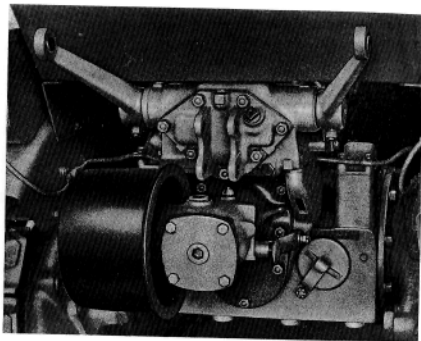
Trattrice equipaggiata di sollevatore idraulico e di puleggia motrice.
